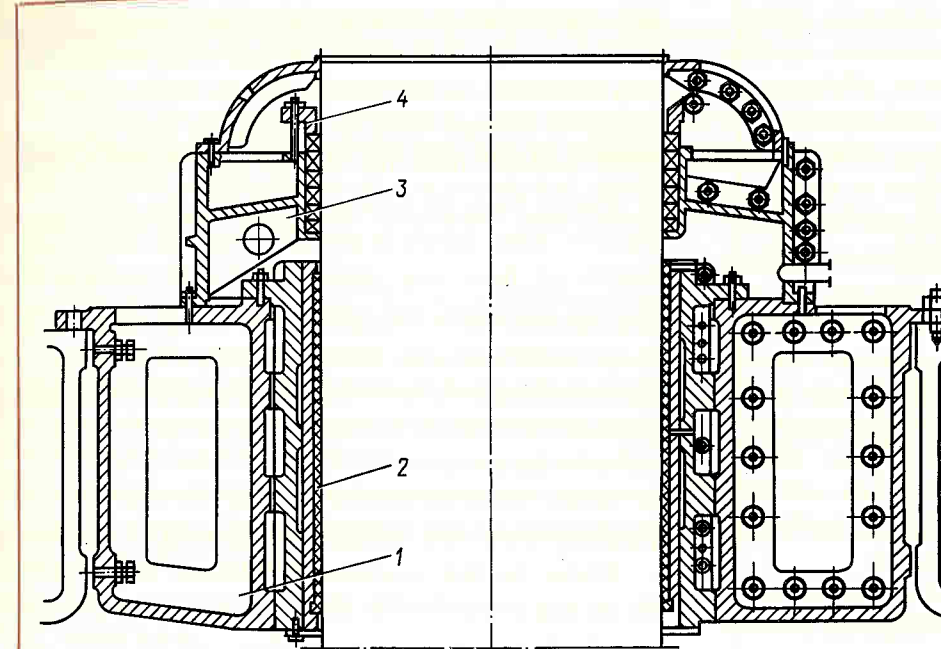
Подшипник гидротурбины с обрезиненным вкладышем
